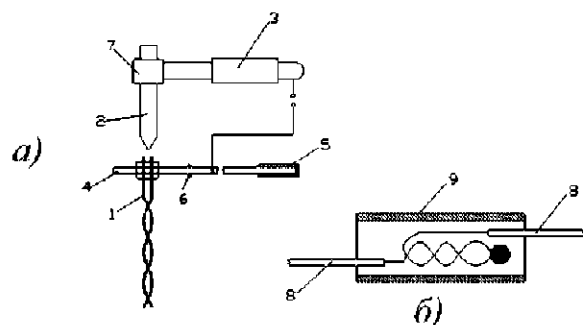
Сварка и изолировка соединений проводов:
